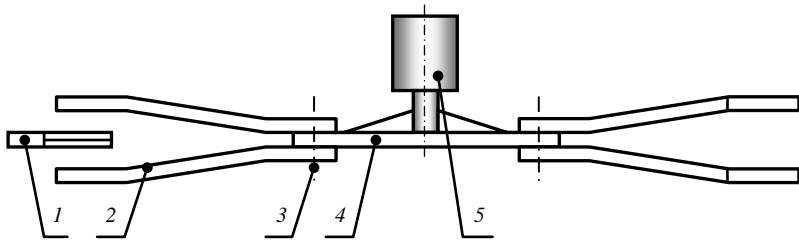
Схема ротора пастбищной косилки Schulte с неподвижным противорежущим ножом: 1 – неподвижный нож; 2 – подвижные ножи; 3 – болты; 4 – несущая часть ротора; 5 – привод
